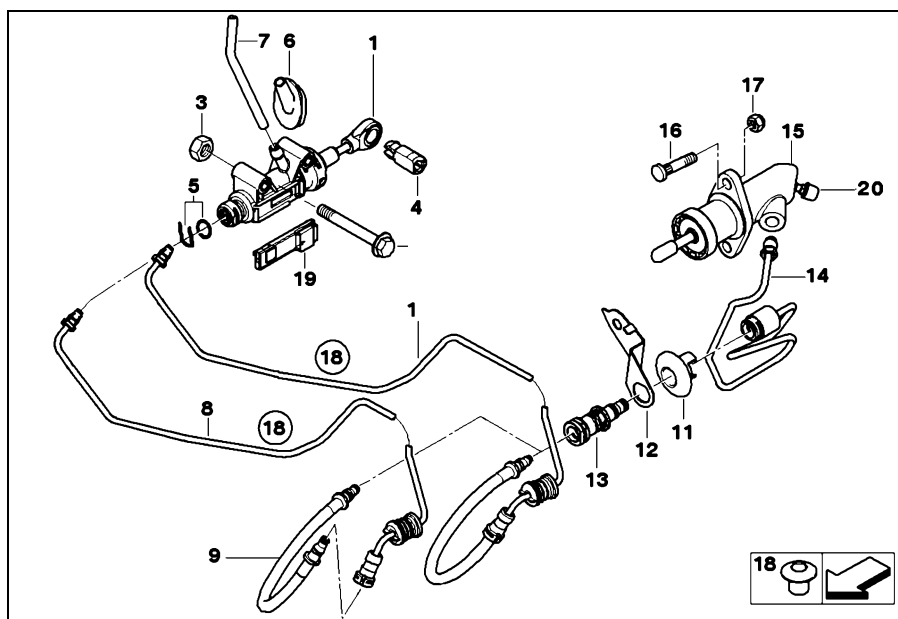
Привод управления сцепления. 1 - главный цилиндр; 2 - палец подвески (болт (М6х45)); 3 - гайка (М6); 4 - штифт; 5 - соединитель с кольцом; 6, 11, 18 - наконечник; 7 - шланг; 8, 10, 14 - трубопровод; 9 - шланг; 12 - держатель; 13 - дроссельный клапан; 15 - рабочий цилиндр; 16 - болт (М8); 17 - гайка (М8); 19 - модуль выключения сцепления; 20 - штуцер прокачки.
